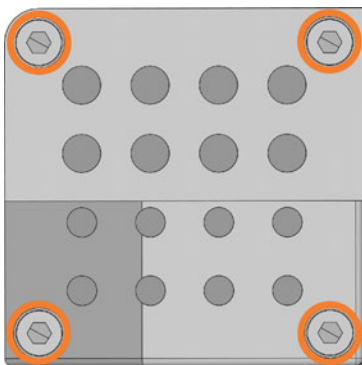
Die 4 Schrauben auf der Unterseite des Werkzeugmagazins (orange markiert)
